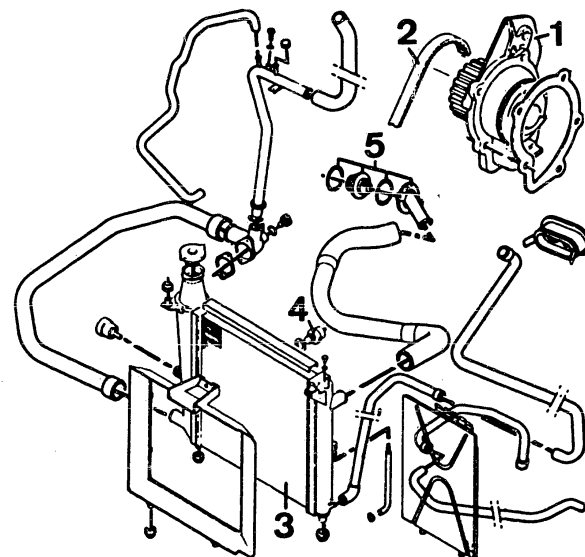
Komponenten des Kühlsystems. 1 Wasserpumpe – 2 Zahnriemen – 3 Kühler – 4 Thermokontakt – 5 Thermostat.
